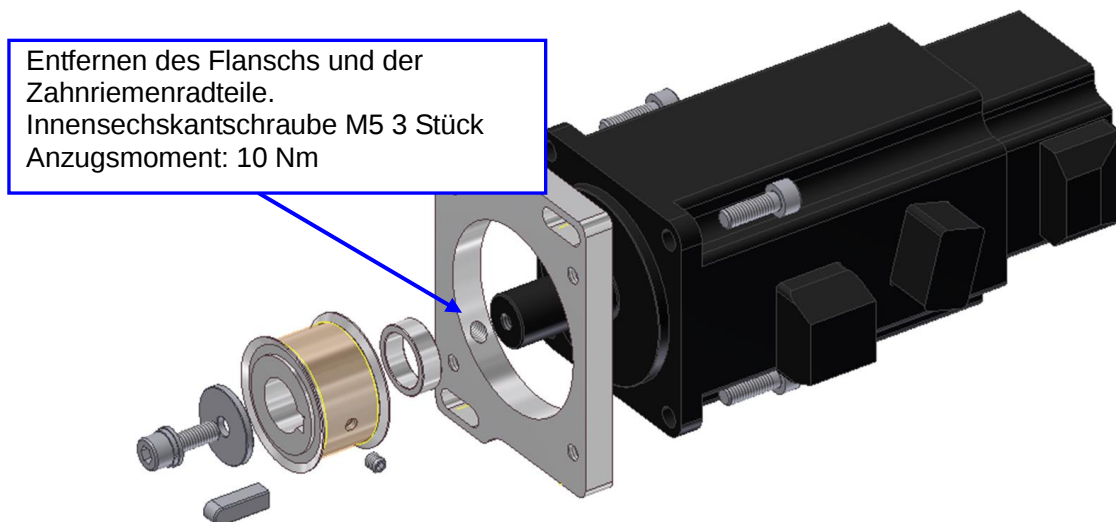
Explosionsdarstellung Z-Achsenmotor
